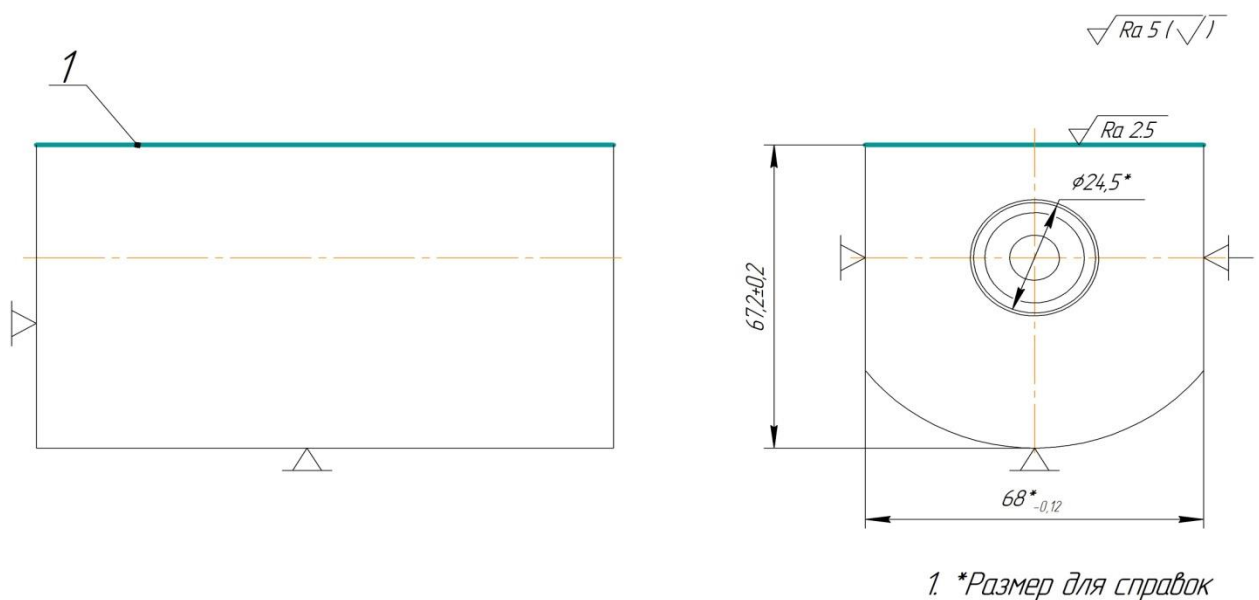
Операционный эскиз фрезерной обработки
